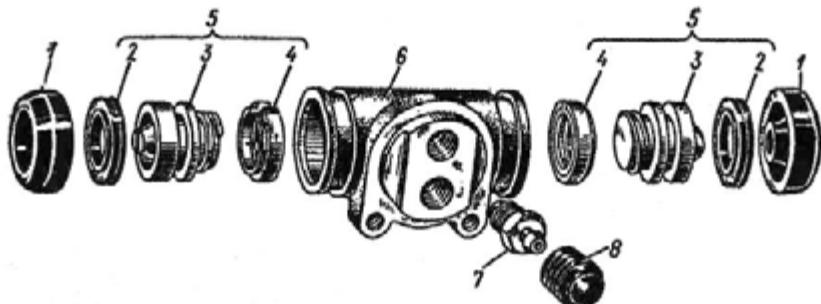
Колесный цилиндр гидропривода тормоза заднего колеса
